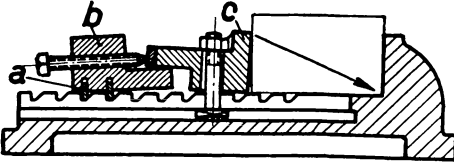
Spindelloser Maschinenschraubstock, Schnitt.
